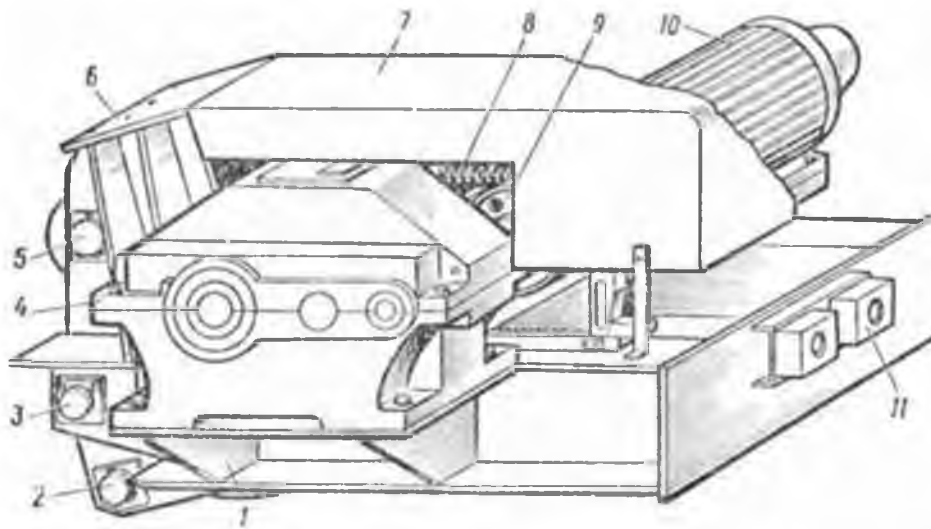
Опорний візок крана ККТ-5: 1-рама; 2 - вісь рейкового захоплення; 3 - вал кріплення опорної стяжки; 4 - редуктор; 5 - вісь монтажних блоків; 6 - плита з'єднання зі стійкою; 7 - кожух; 8 - гальмівний пристрій; 9 - шків; 10 - електродвигун; 11 - гумовий буфер
